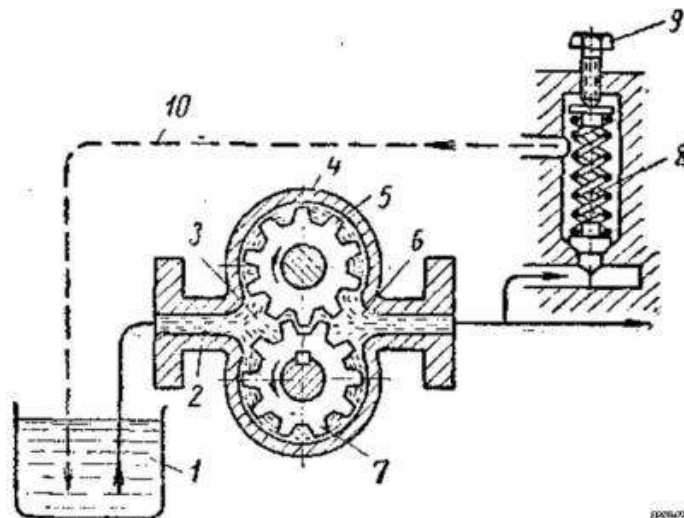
Схема установки шестеренчатого насоса: 1 — масляный бак; 2 — приемный патрубок; 3 — всасывающая полость; 4 — корпус; 5 — ведомая шестерня; 6 — нагнетательная полость; 7 — ведущая шестерня; 8 — перепускной клапан; 9 — регулировочный винт клапана; 10 — сливной маслопровод.
